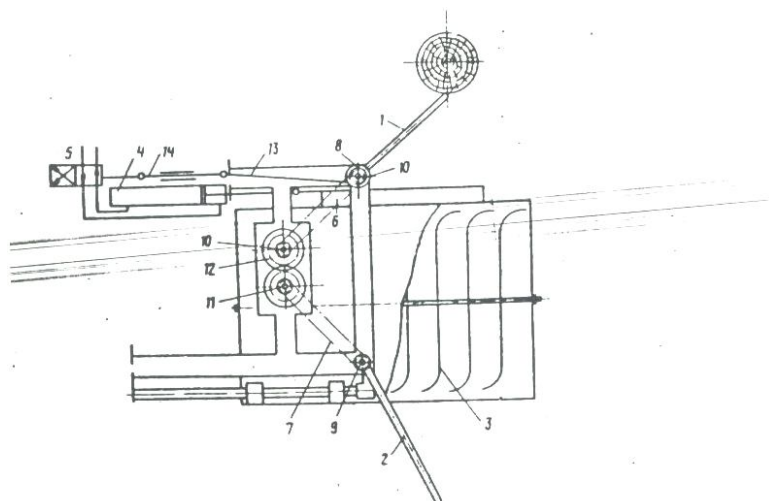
Гидравлическое следящее устройство рабочего органа с двумя кинематически связанными стержнями сигнального шупа: 1-2 – стержни шупа; 3 – рабочий орган; 4-5 – гидроцилиндр и гидрораспределитель; 6-7 – цепные передачи; 8,9,10 и 11 – звездочки; 12 – зубчатая передача
